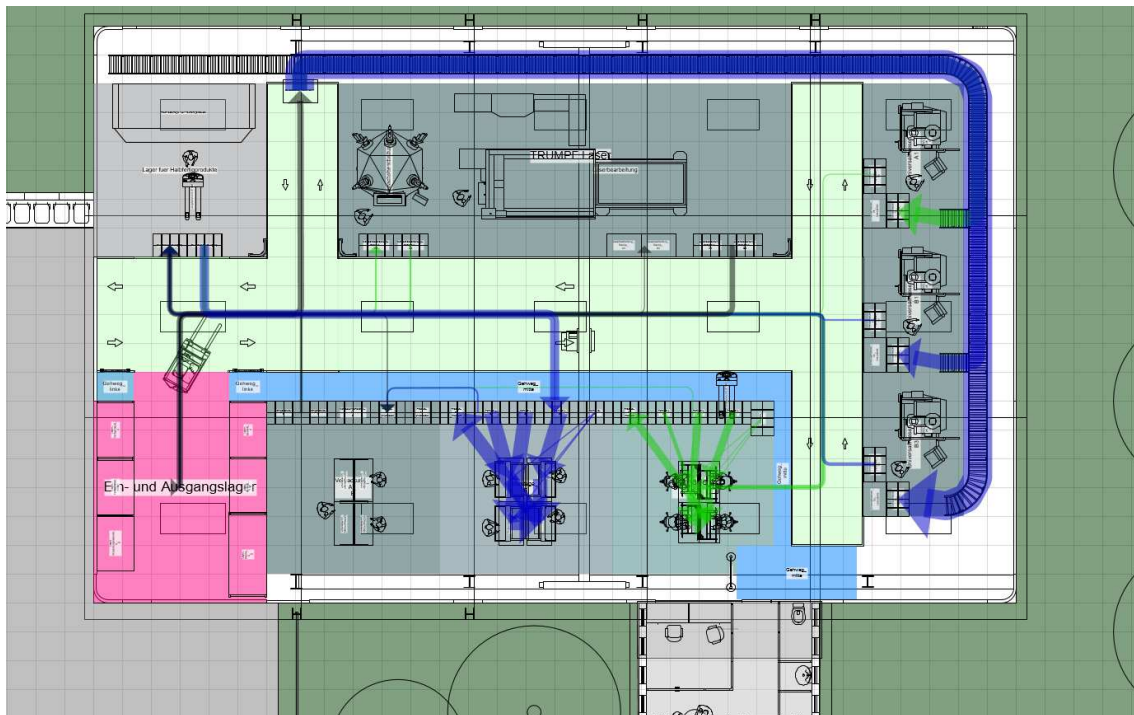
Grundriss Use Case Beispielfabrik
